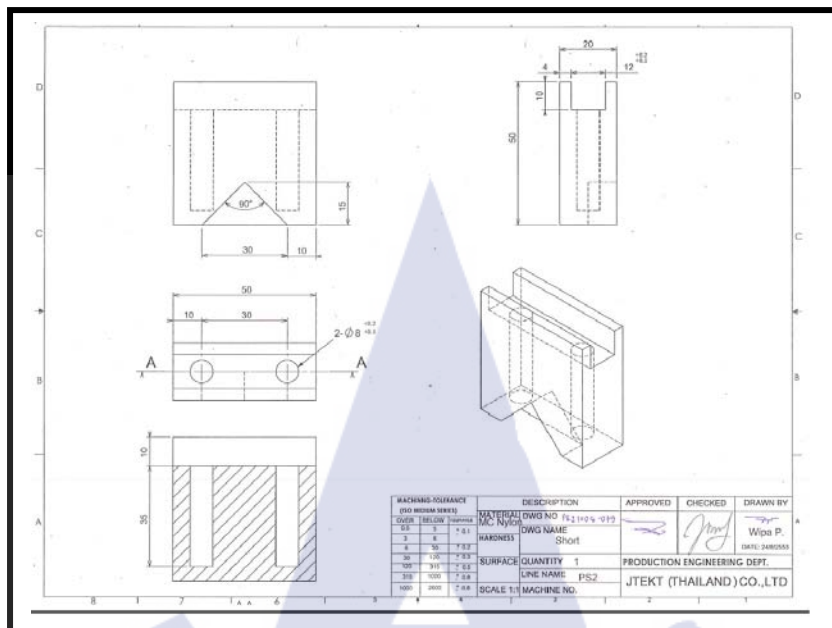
แสดงแบบประกอบ Jig support เครื่อง Deburring
